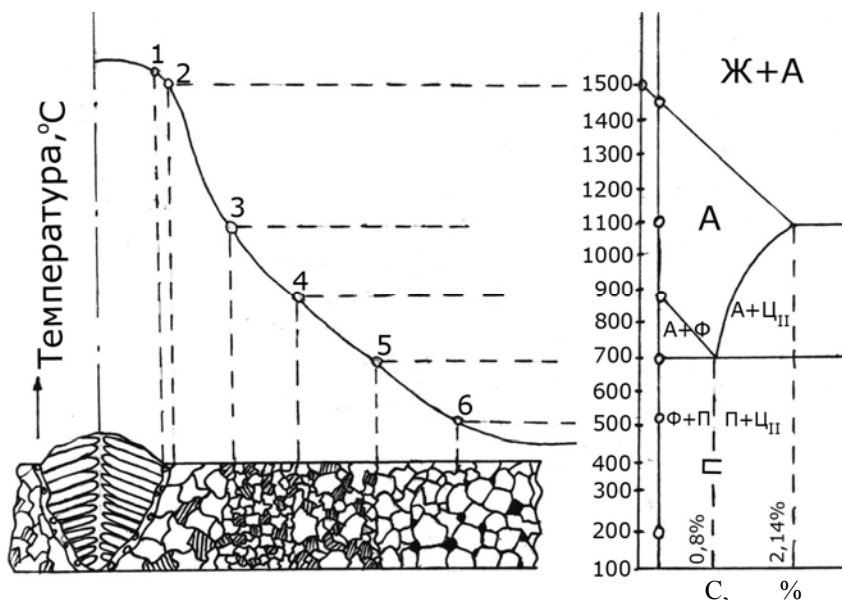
Строение сварного шва при сварке низкоуглеродистых сталей
